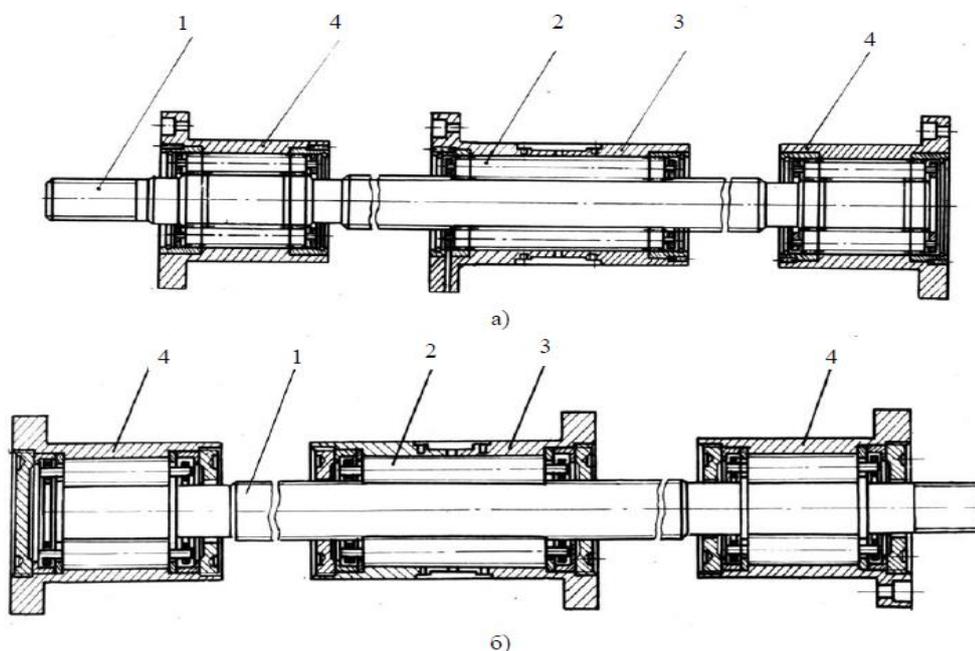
Передачи с короткими резьбовыми роликами с опорными гайками, имеющими дополнительные связи
